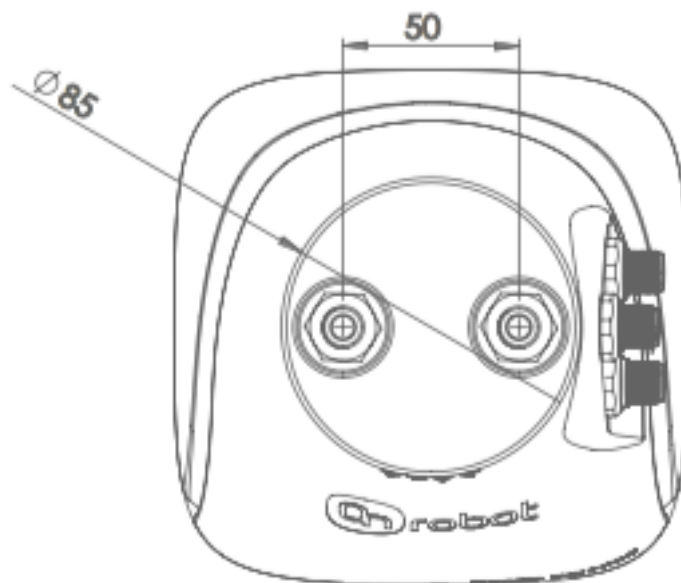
Dimensões da superfície de montagem (parte superior) do Gecko Gripper.
